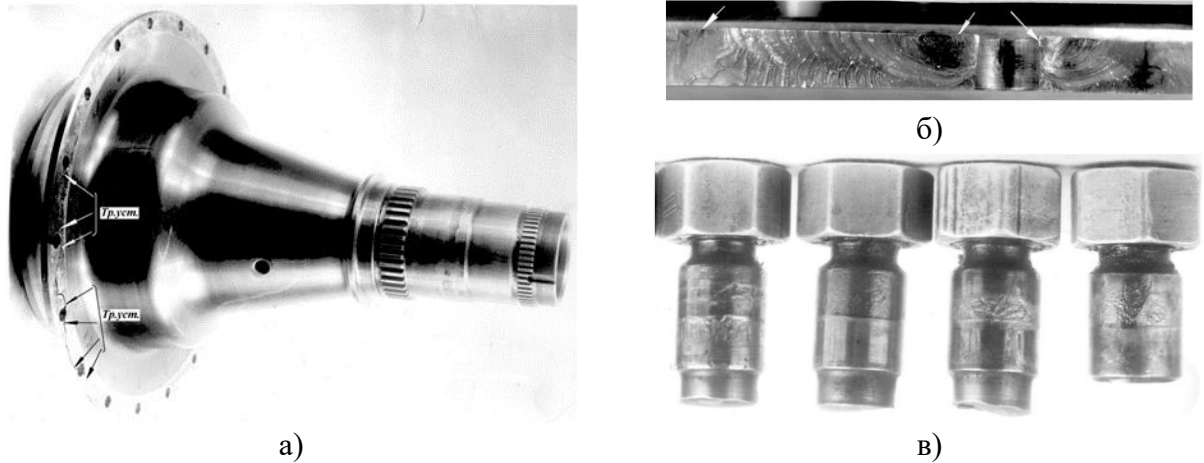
Разрушение от фреттинга вала-шестерни редуктора и втулки НА с очагами расположения фреттинг-повреждений (стрелками указаны очаги разрушений) [2].
